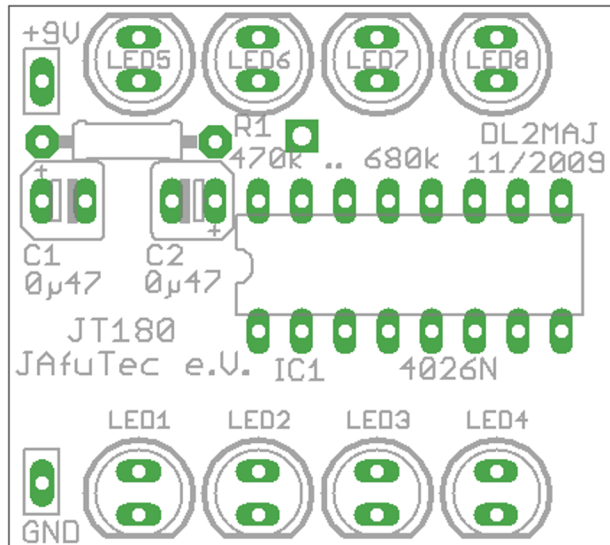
Bestückungsplan für bedrahtete Bauelemente
